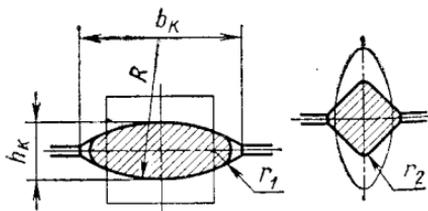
Калибровка по схеме квадрат—овал—квадрат
